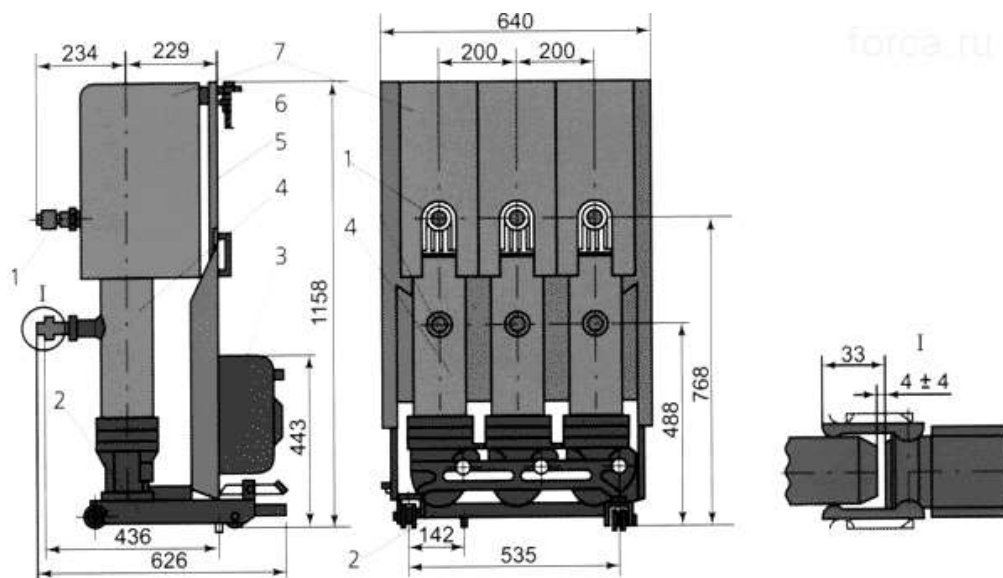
Малооливовий колонковий вимикач ВК-10: 1 - роз'ємний контакт висувного елемента; 2 - рама візка; 3 - привод; 4 - полюс вимикача; 5 – фасадна перегородка; 6 - штепсельний роз'єм; 7 - ізоляційний кожух.
